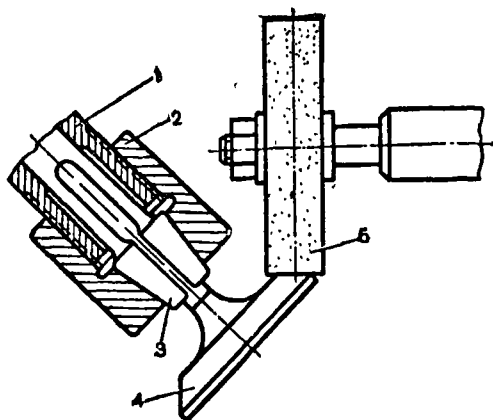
Установка клапана в цанговом зажиме: 1 — корпус цангового зажима; 2 — гайка; 3 — цанга; 4 — клапан; 5 — шлифовальный круг
